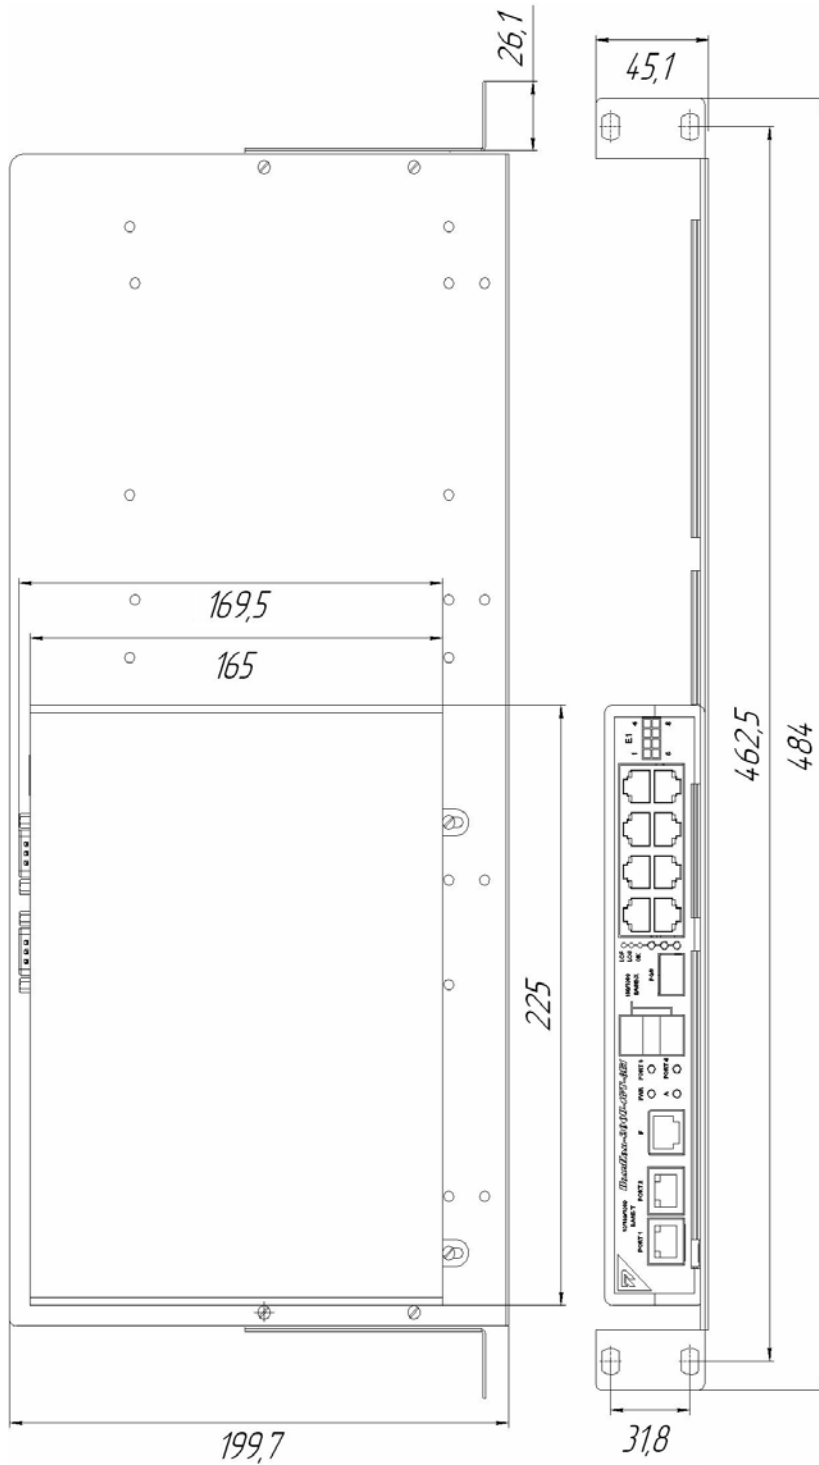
Габаритные и установочные размеры АЛТ с пластмассовым корпусом
